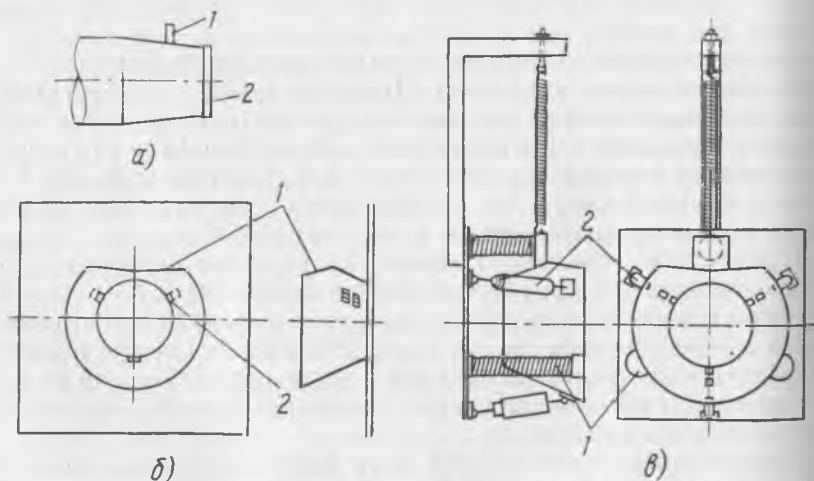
Стыковочный механизм с коническими поверхностями:
